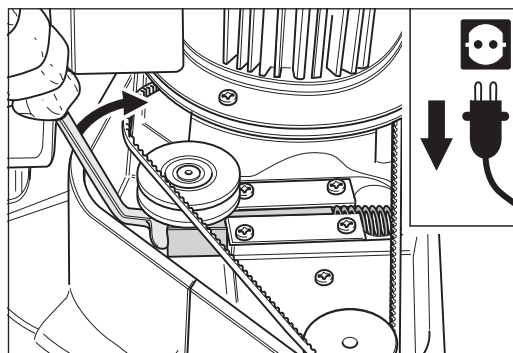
Den Keilriemenspanner vorsichtig entspannen und den Ringschlüssel entfernen.
